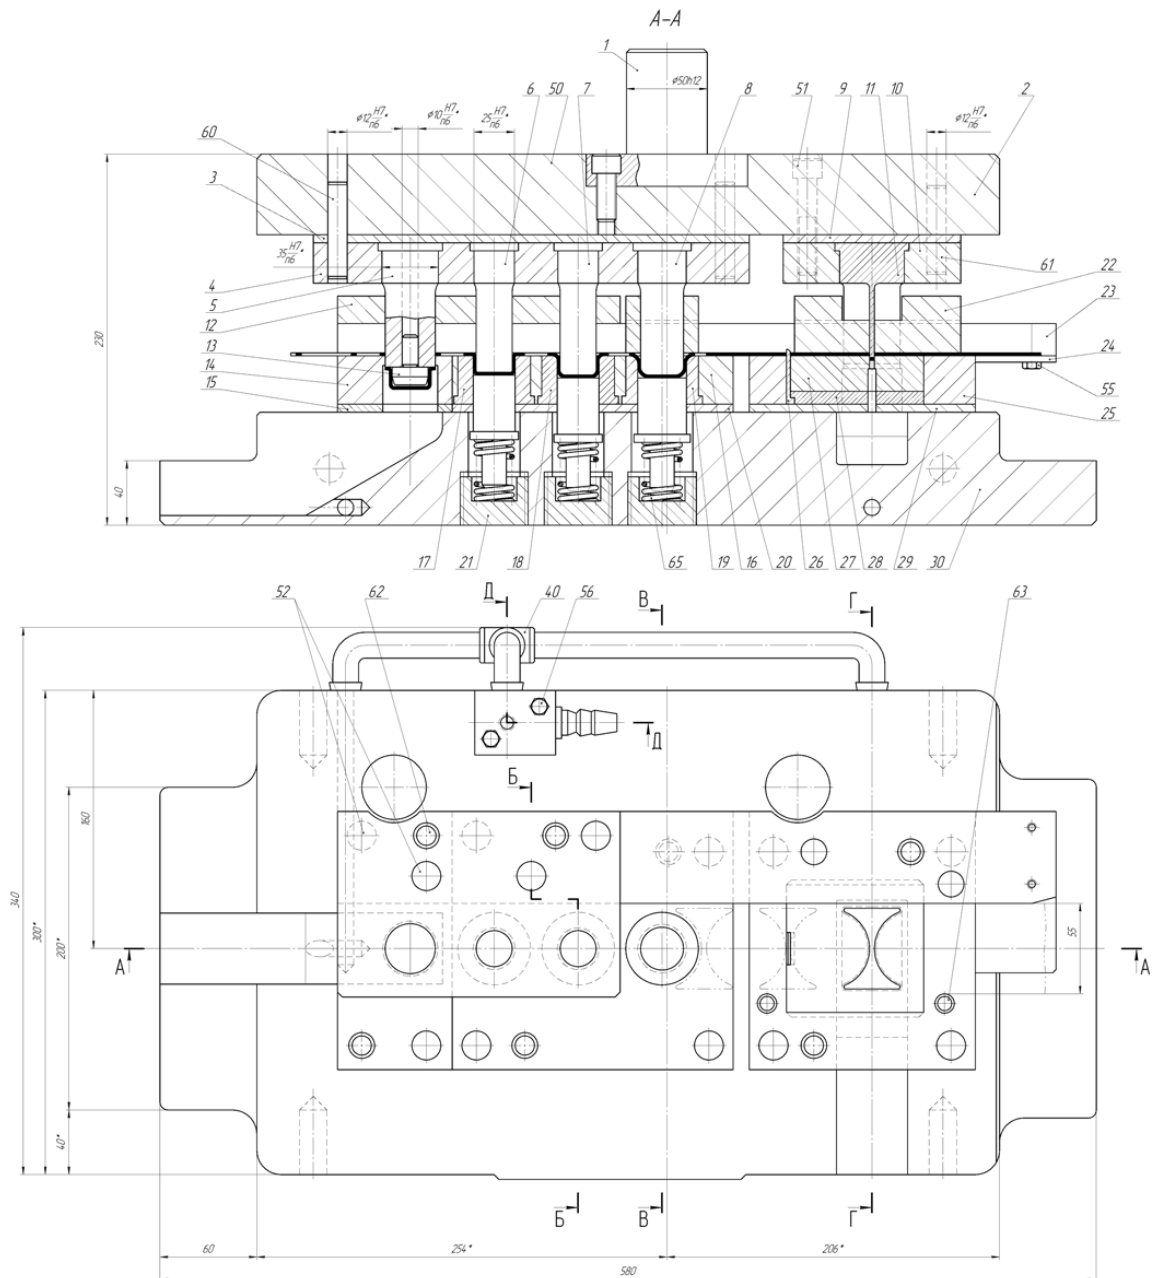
Штамп послідовної дії для витяжки деталі «Футорка»
